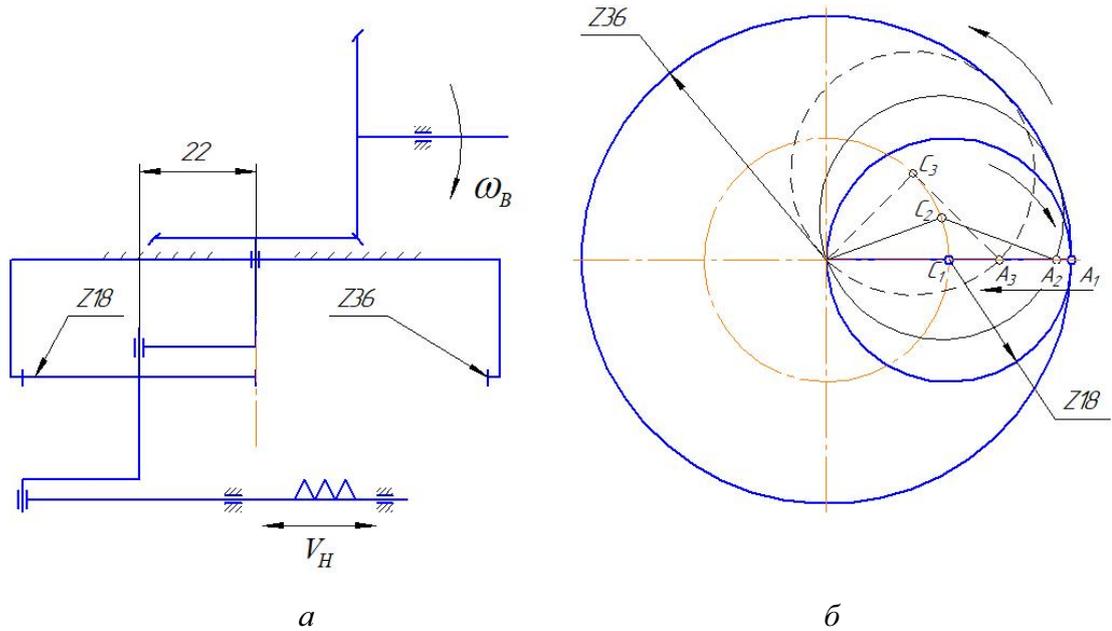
Кинематическая схема планетарного механизма (а) и фрагмент, обосновывающий движение ножа (б)
